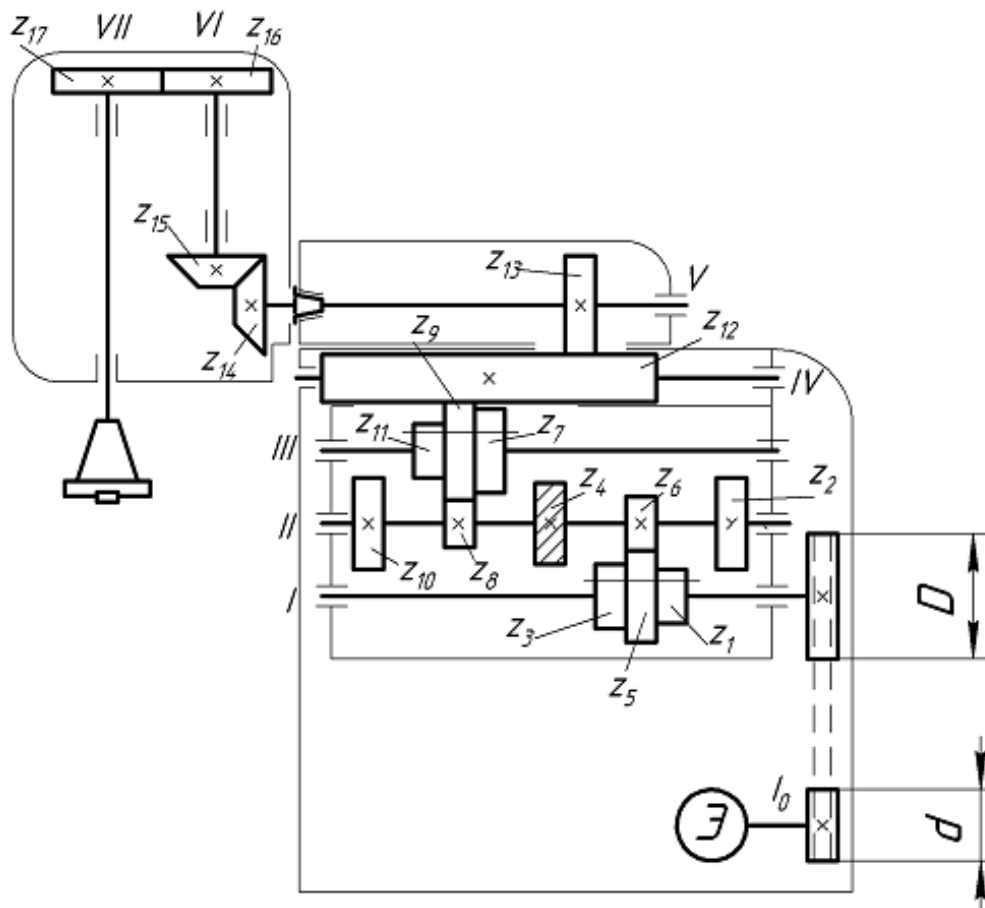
Кінематична схема привода головного руху широко універсального фрезерного верстата
